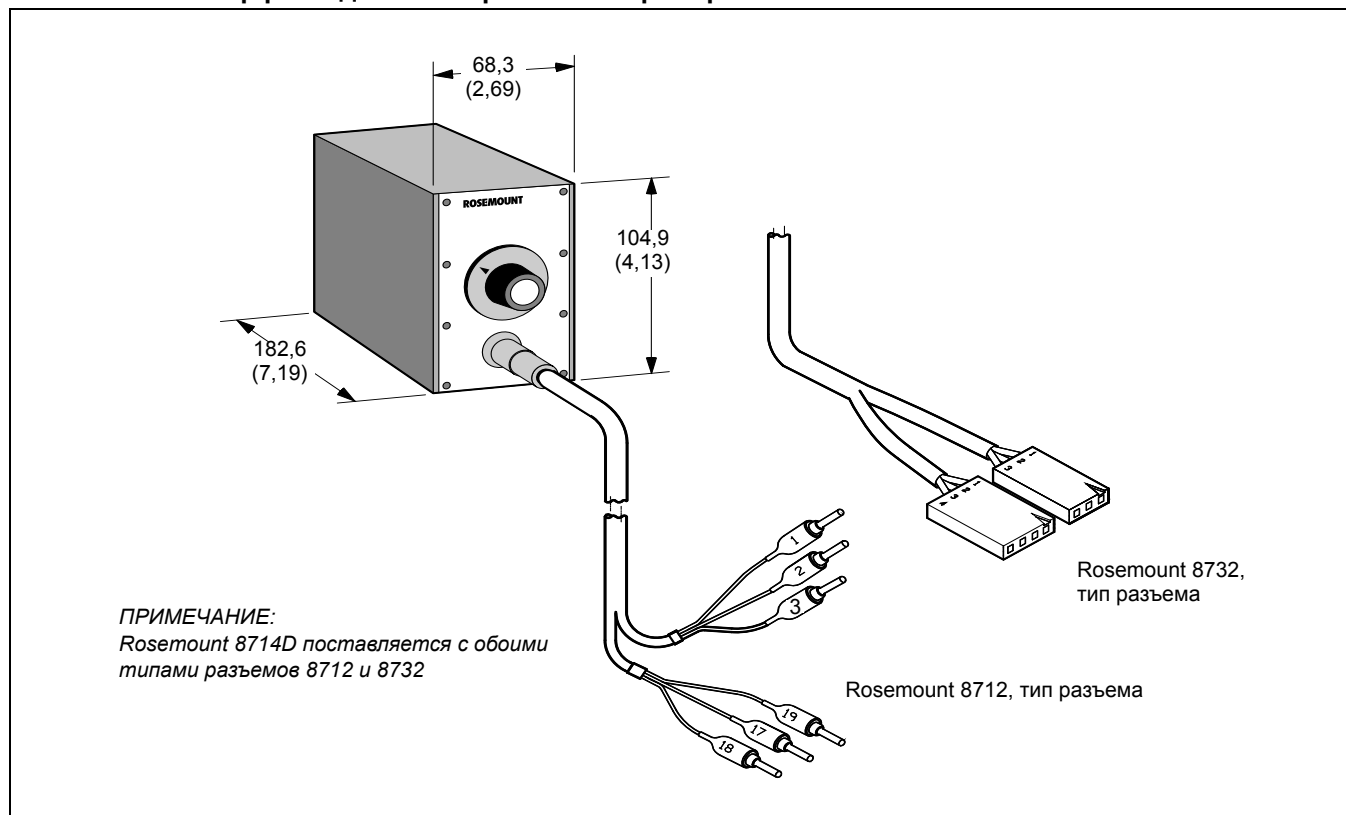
Имитатор расхода – Калибровочный прибор Rosemount 8714D
